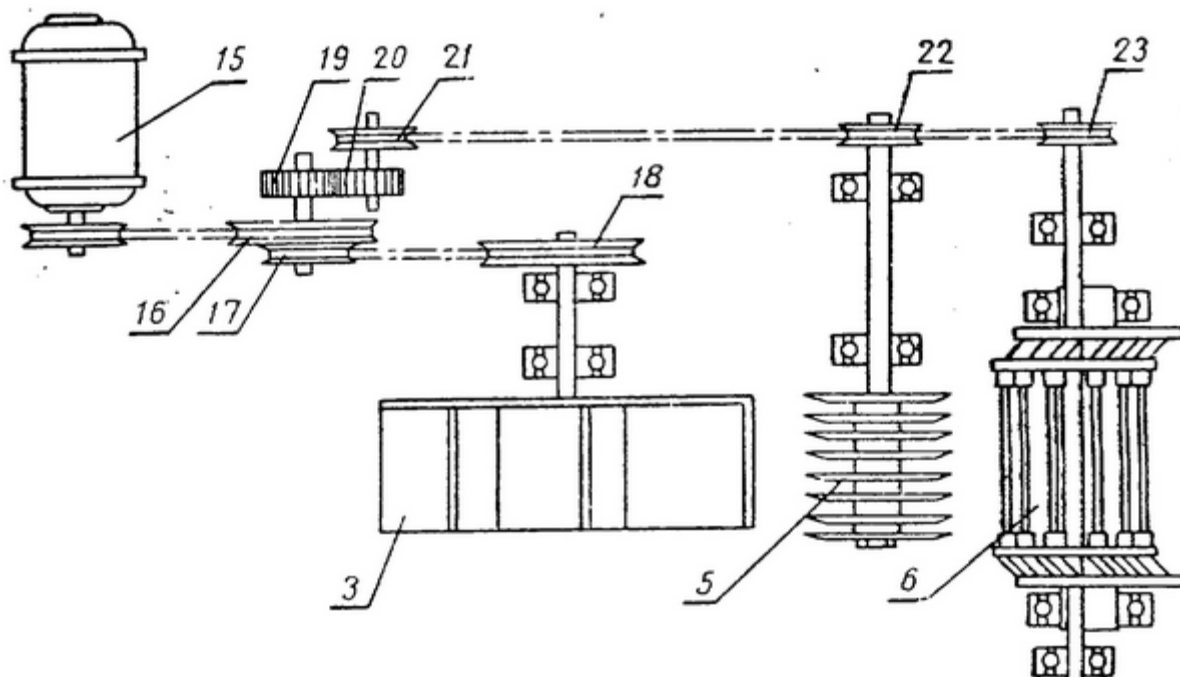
Кінематична схема машини для різання овочів марки RU-3.
